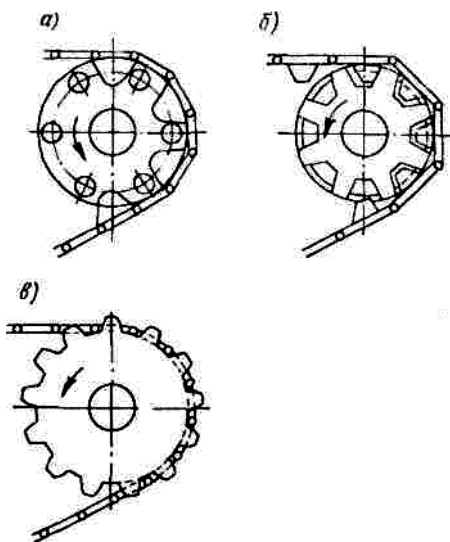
Типы зацеплений ведущего колеса с гусеницей
